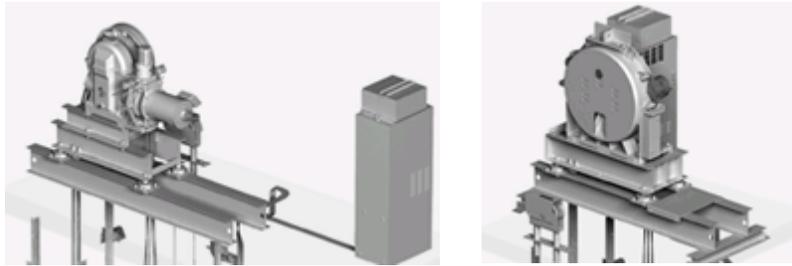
Máquina de Tracción con Engranajes y Máquina de Tracción sin Engranajes
